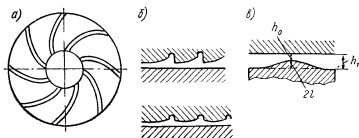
Формы боковых поверхностей шипов и подшипников
